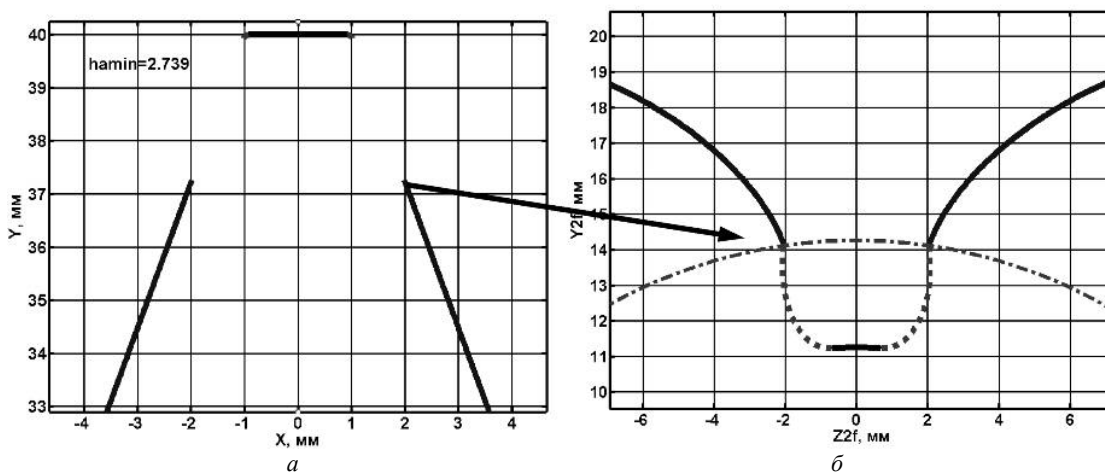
Робоча частина бічного профілю твірної черв'ячної фрези а) і профіль зубчатого колеса сформований такою фрезою б).  $m=3, d_a=80, r_{a0}=0.1$ , фреза коволютна,  $Z_k=10, x=0, \beta_k=0^0$
